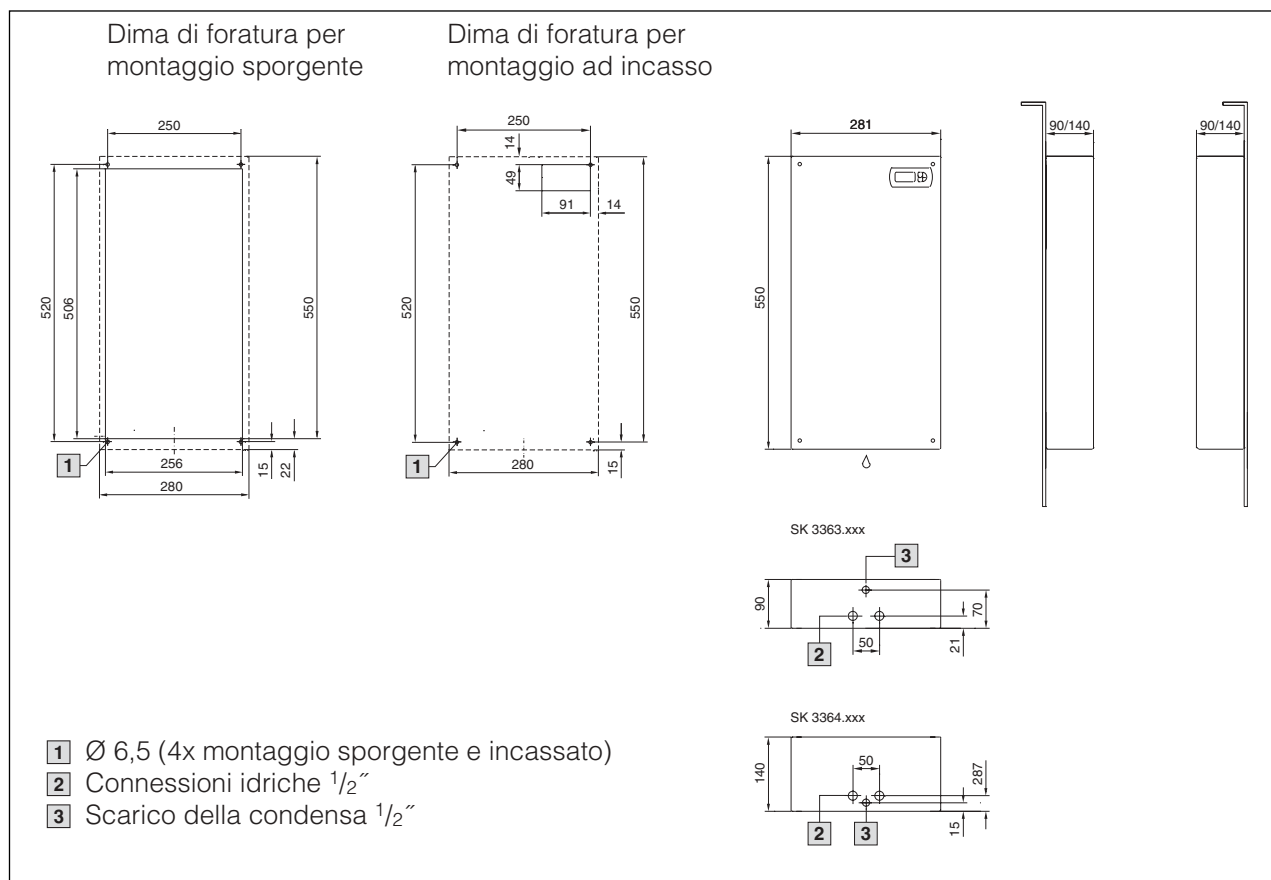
SK 3363.xxx/SK 3364.xxx montaggio sporgente
